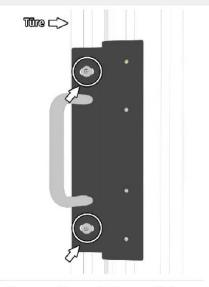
Montageplatte mit Ankerplatte am Profil anbringen und zur Prozesszuhaltung ausrichten. Schrauben M8 x 12 mm Torx festziehen.
